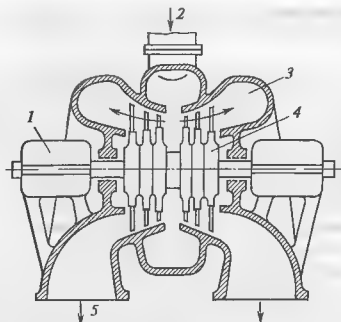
Конструктивная схема двухпоточного ЦНД
